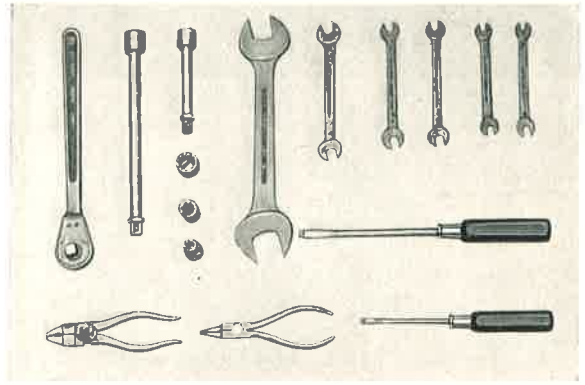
Zusammenstellung der Werkzeuge, wie sie für die Arbeit Gruppe M, Motor, M 2 gebraucht werden.
